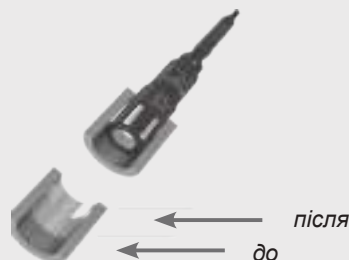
Якість внутрішньої поверхні до та після пластичного деформування
